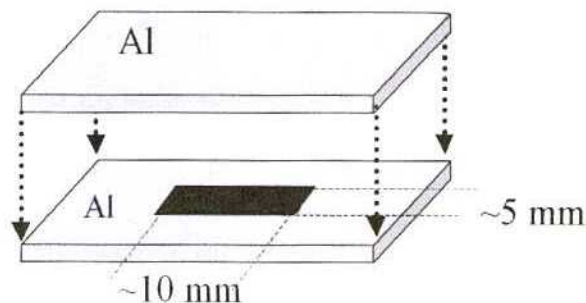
Esquema de la preparación, para la soldadura, del dispositivo a irradiar.
